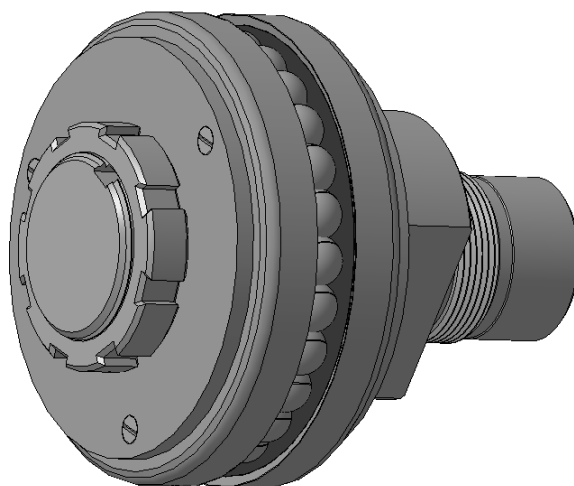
Внешний вид модельного образца инструмента для суперфинишной ПЦО
